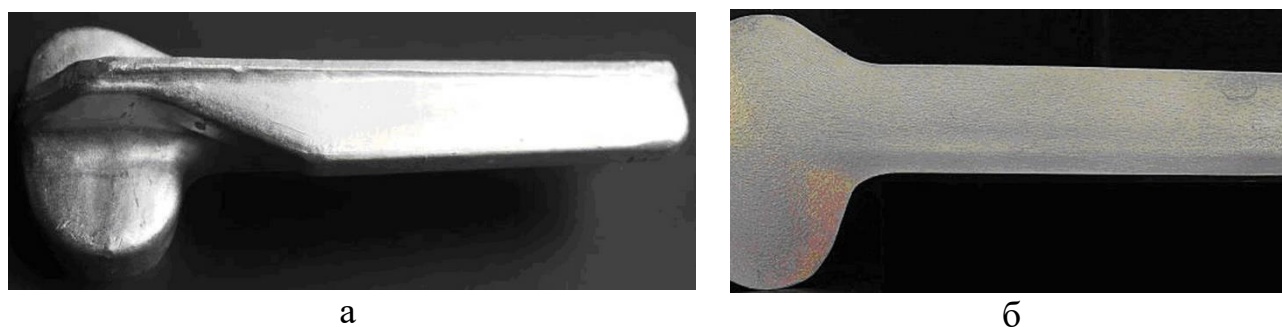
Деталь «Кронштейн» першої групи типових представників заготовок, що вальцюються на кувальних вальцях: штампована поковка (а); макроструктура поздовжнього перерізу заготовки, що вальцюється під штампування (б)
